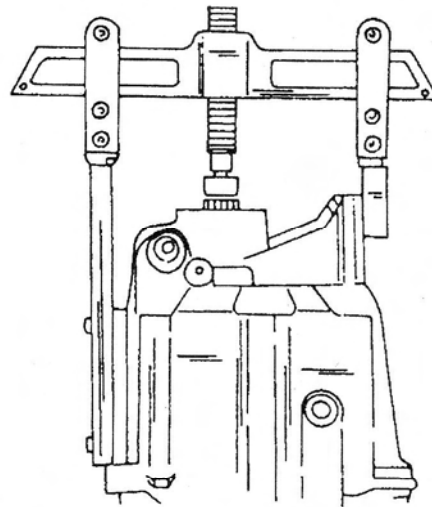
Отжать заднюю крышку от коробки передач показанным способом. Из-за запрессованного шарикового подшипника крышка туго сидит на коробке.
